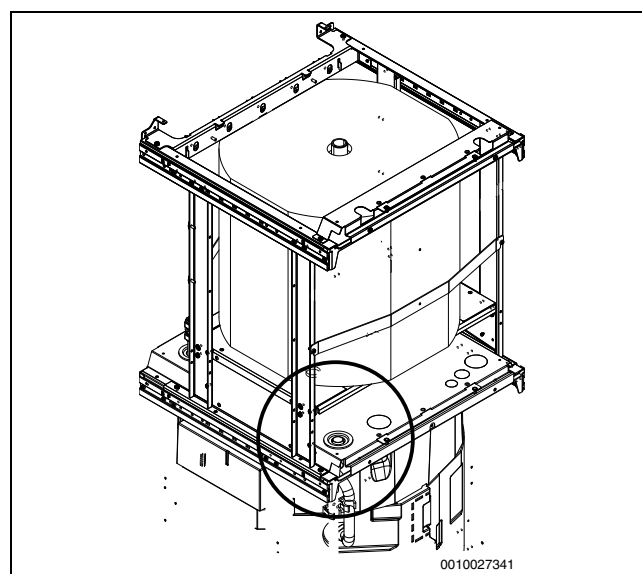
Montage d'un nouveau tuyau de raccordement (n° 10)
